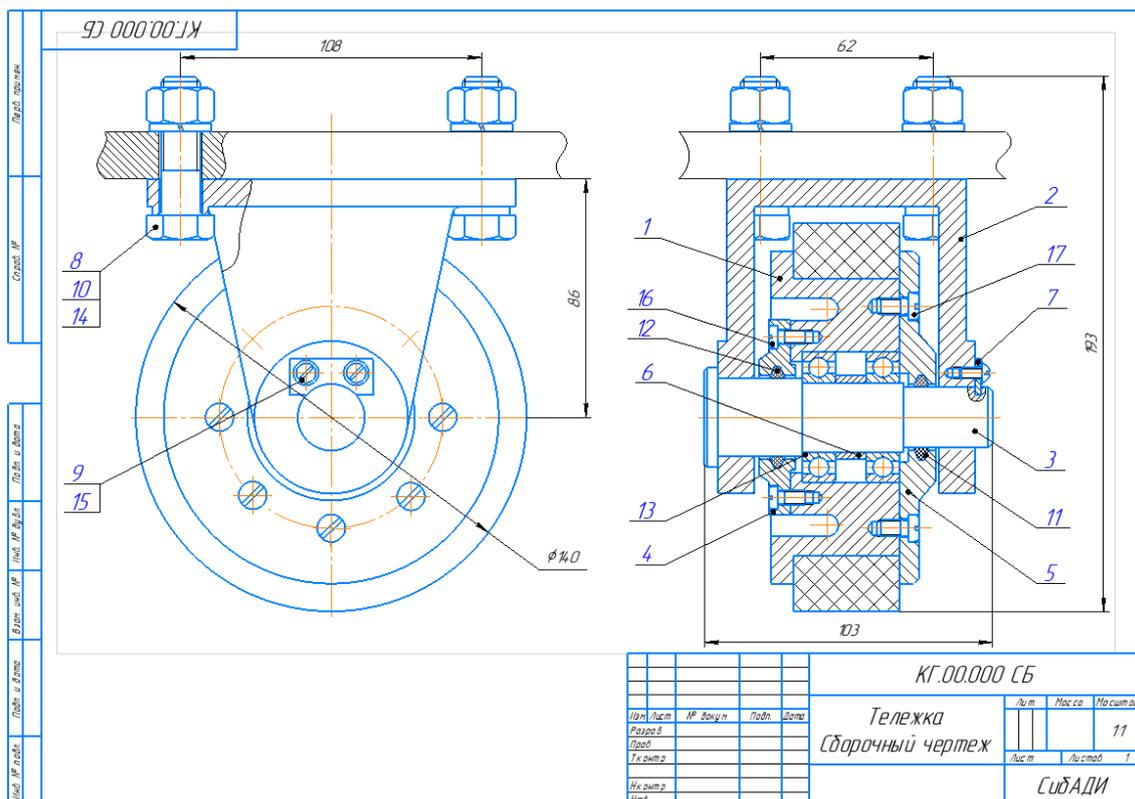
Сборочный чертёж «Тележка» с размерами
